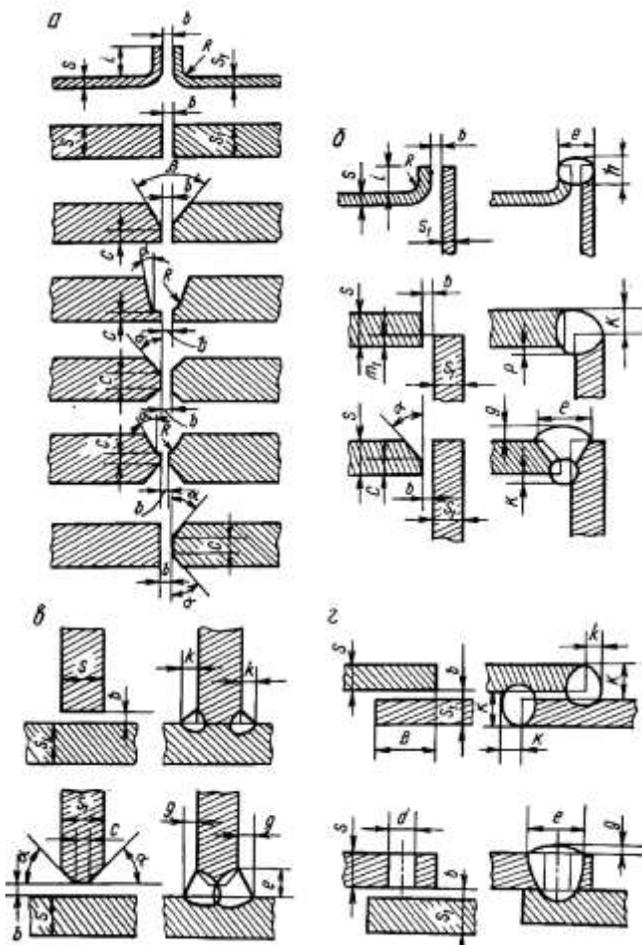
Элементы геометрической формы подготовленных кромок под сварку: а – стыковых швов; б – угловых; в – тавровых; г – нахлесточных швов; б – зазор; В – размер нахлестки; с – притупление; d – диаметр отверстия; e – ширина шва; k – катет шва; t_1 – величина смещения кромок; S и S_1 толщина металла; q – выпуклость шва; α – угол скоса кромки; β – угол разделки кромок
